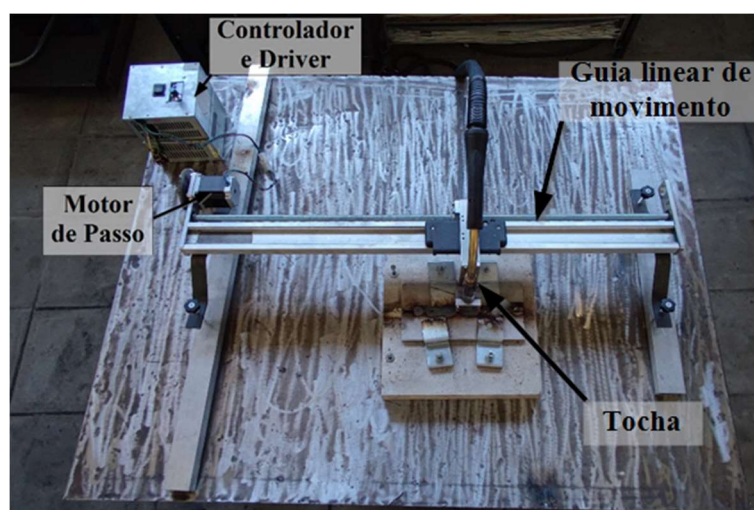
Mesa com guia mecanizada do processo de soldadura.
